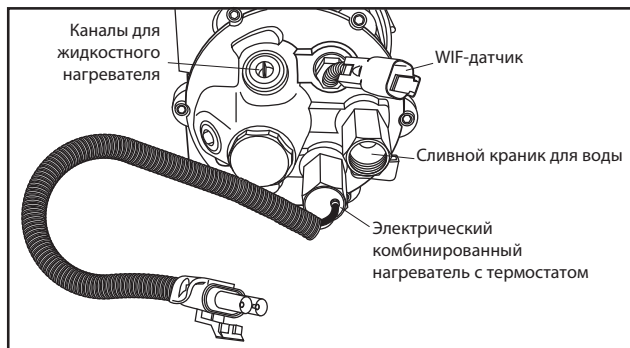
Электрический комбинированный нагреватель и расположение WIF-датчика
